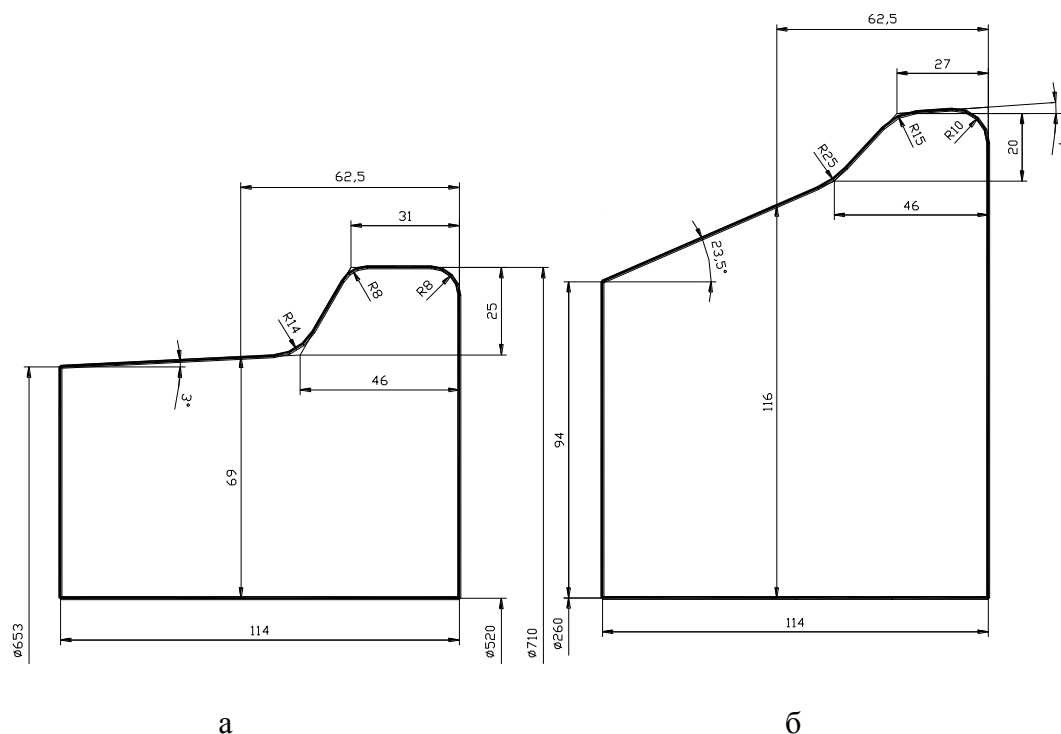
Контуры радиальных сечений фланца (а) и кольцевой заготовки (б)
